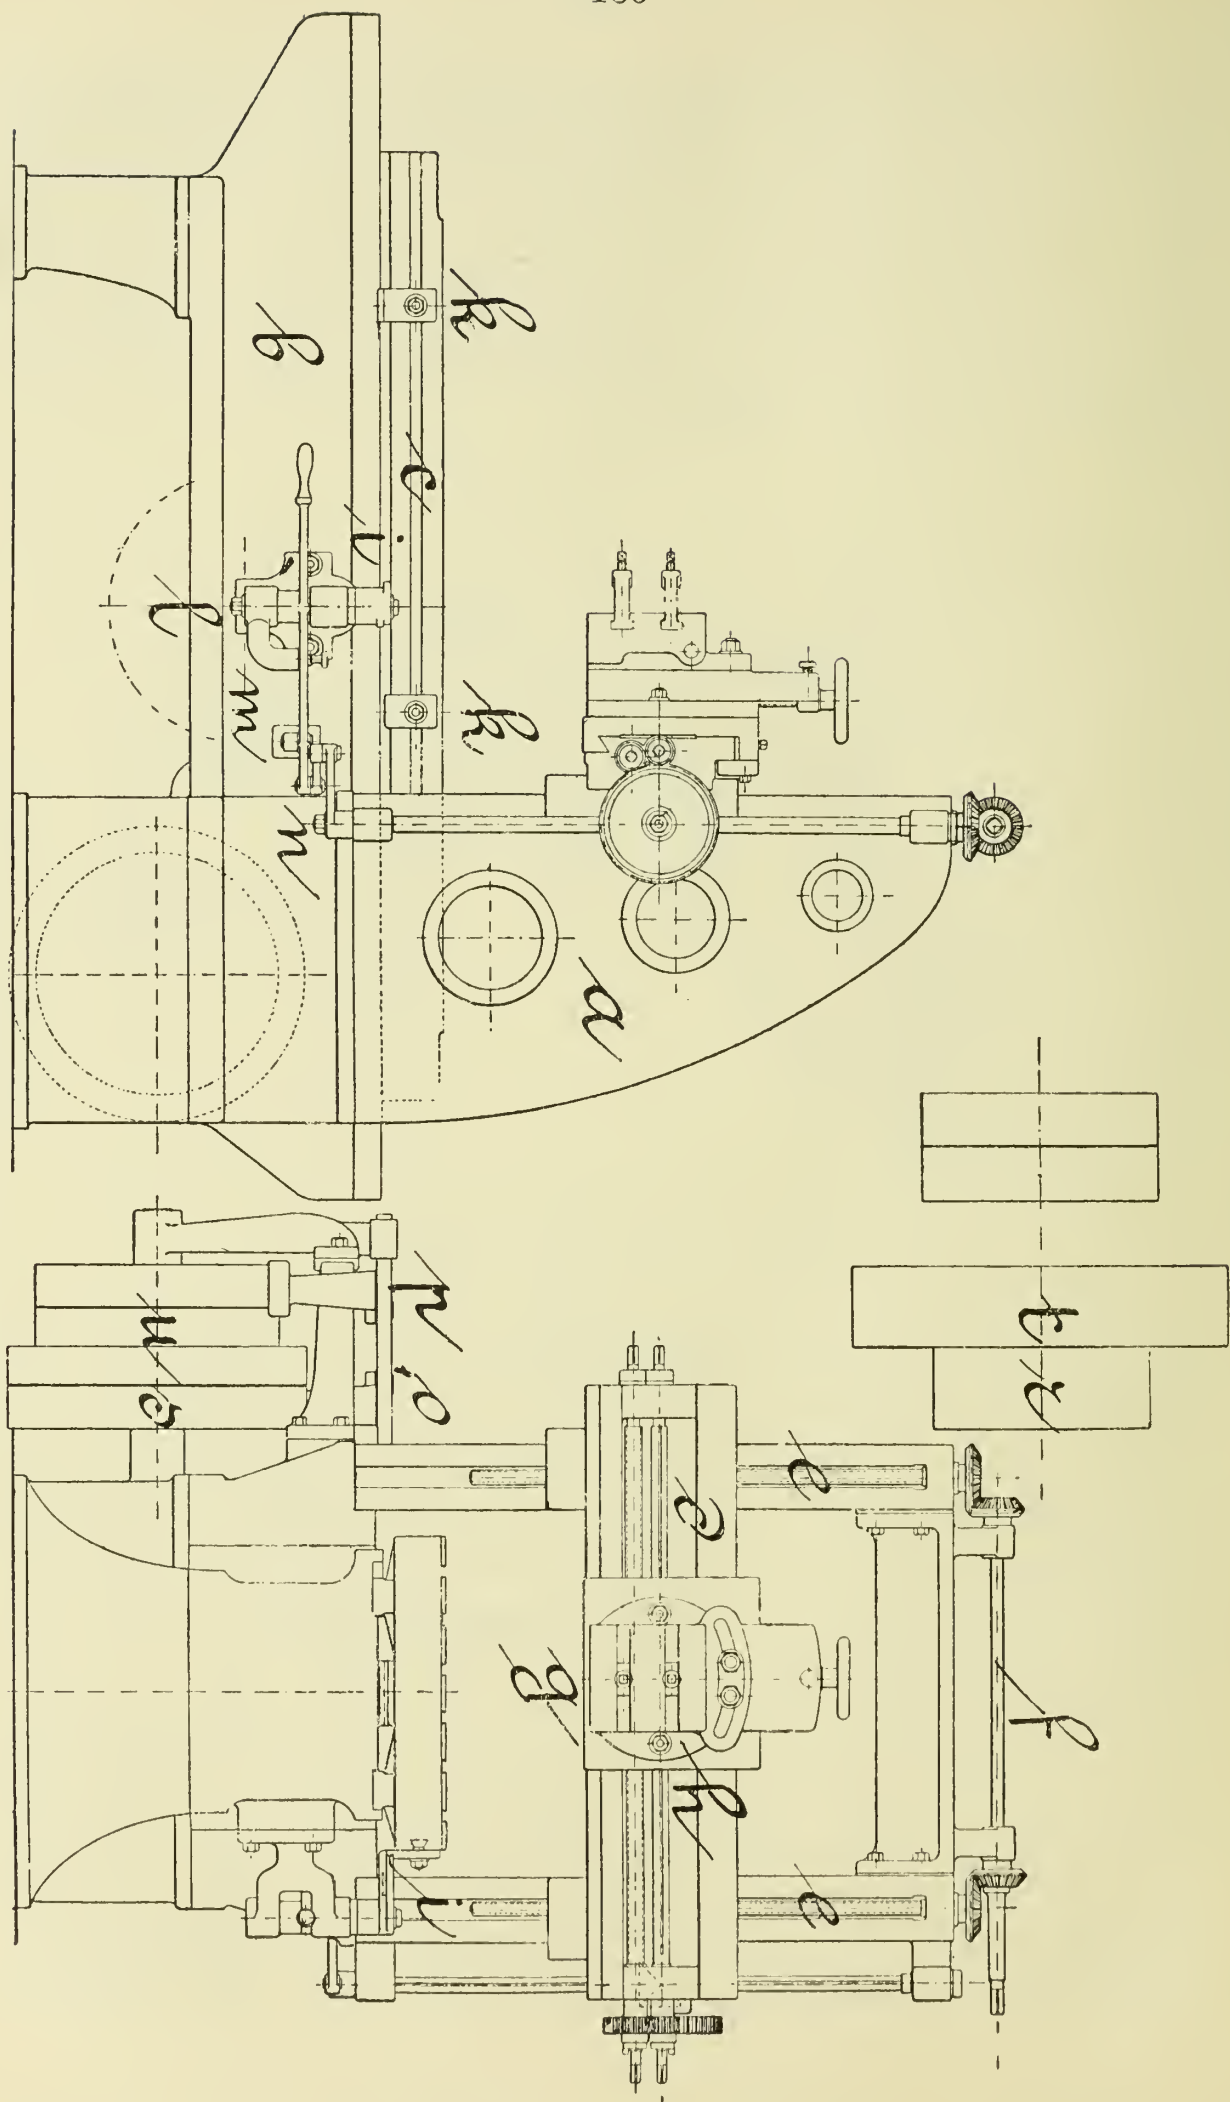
Hobelmaschine der Maschinenfabrik Ludwigshafen.
